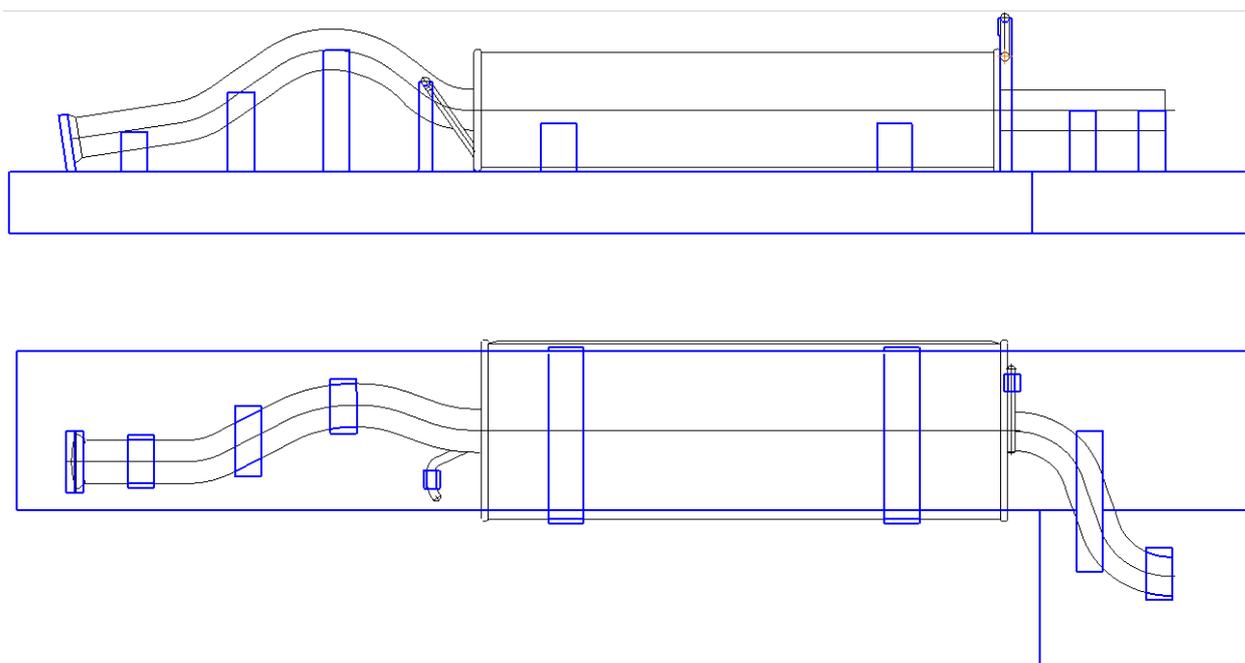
Эскиз сборочного кондуктора с глушителем
